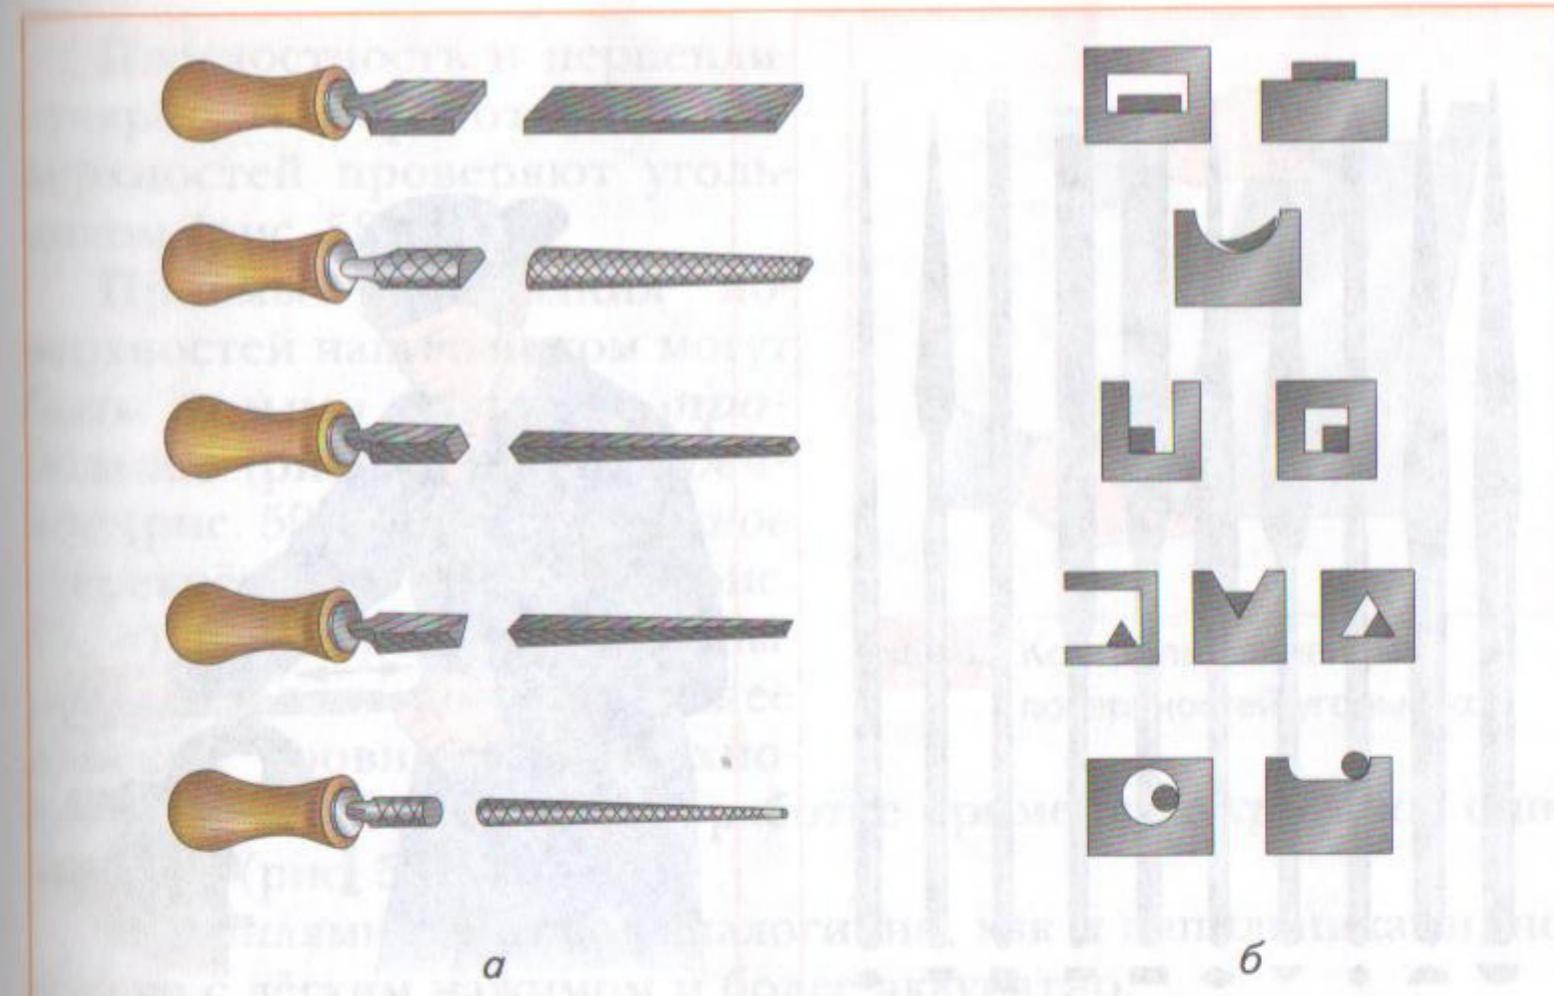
Виды напильников (сверху вниз): а — прямоугольный (плоский), полукруглый, квадратный, треугольный, круглый; б — получаемые ими профили поверхностей
